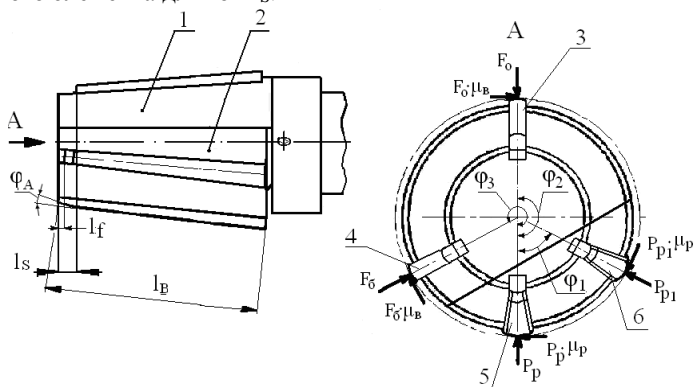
Схема абразивно-выглаживающей развертки:
